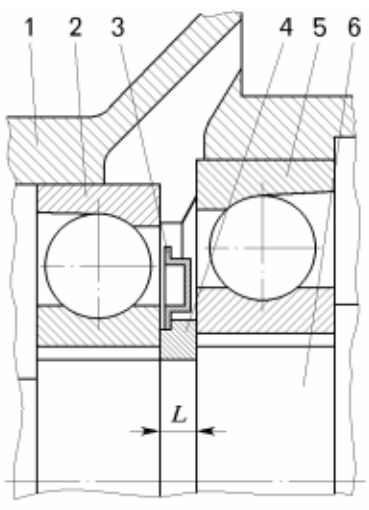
Картер подшипников ведущей шестерни главной передачи:
